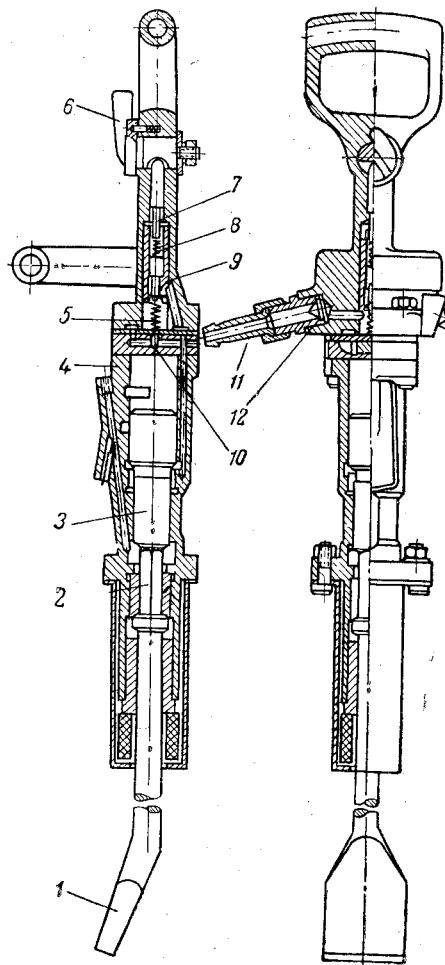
Общий вид и разрез пневматической шпалоподбойки ША-19:
